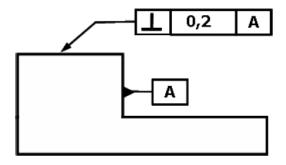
Indicação de tolerância de perpendicularidade em desenho técnico
